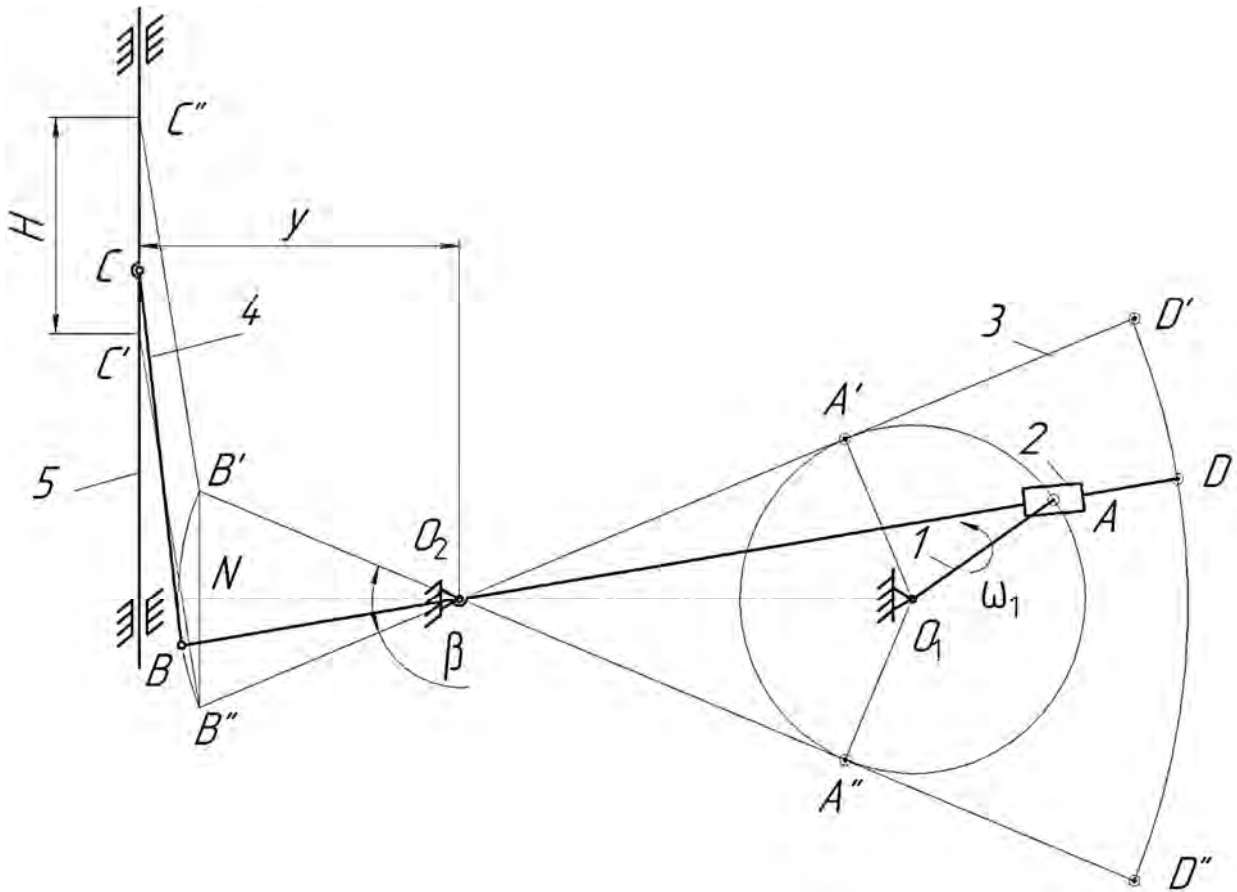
Схема механизма долбежного станка (для примера 6)
